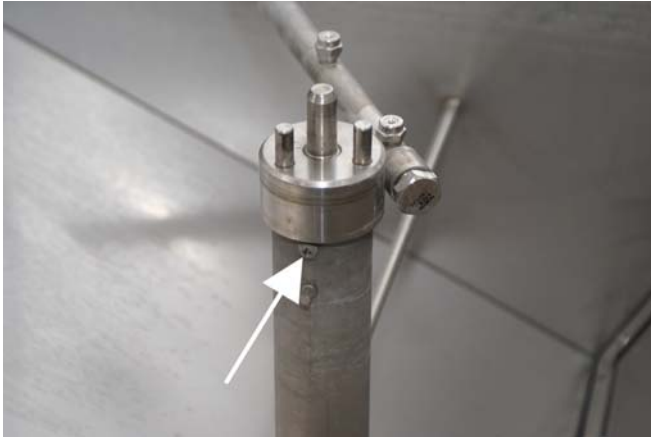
Halteschrauben für Lager, vordere Schraube
